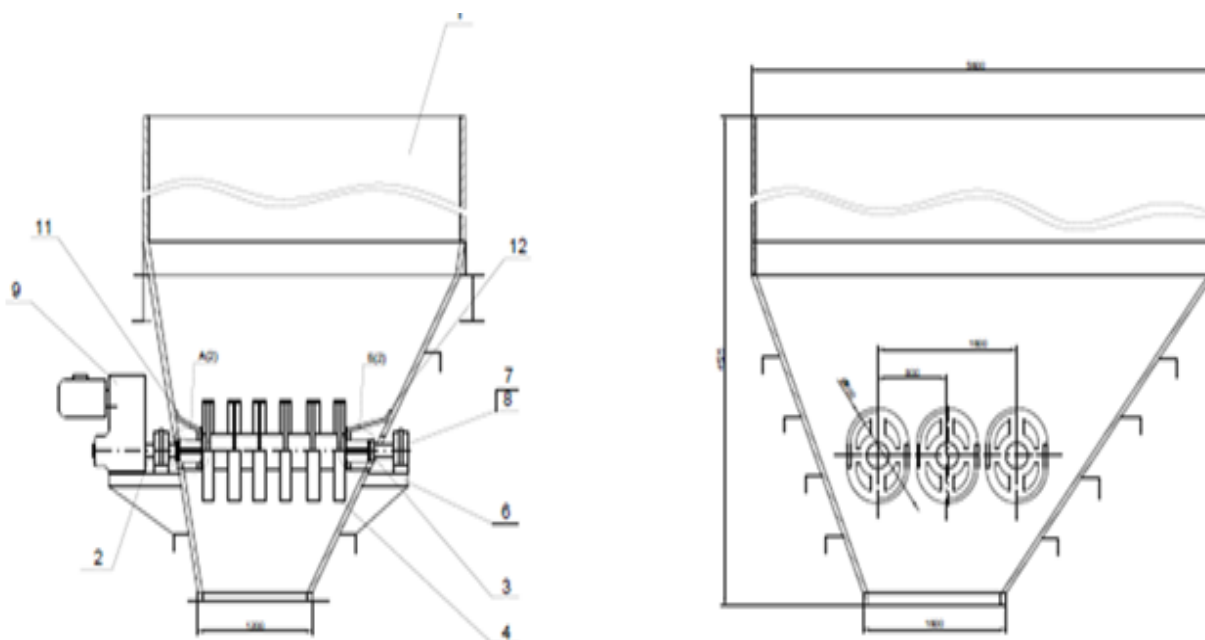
Общий вид ворошителя: 1- бункер; 2- вал редуктора; 3-вал с продольным пазом; 4-вал кулачковый; 5- кулачок; 6-рама; 7-подшипниковая опора; 8-подшипник; 9- мотор-редуктор; 10-муфта; 11-защитный кожух меньший; 12- защитный кожух больший; 13- защитная пластина
